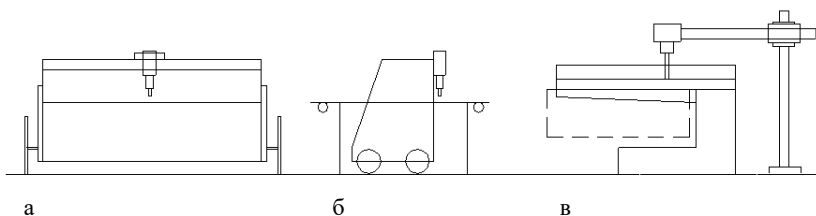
Установки для сварки прямолинейных сварных соединений:
